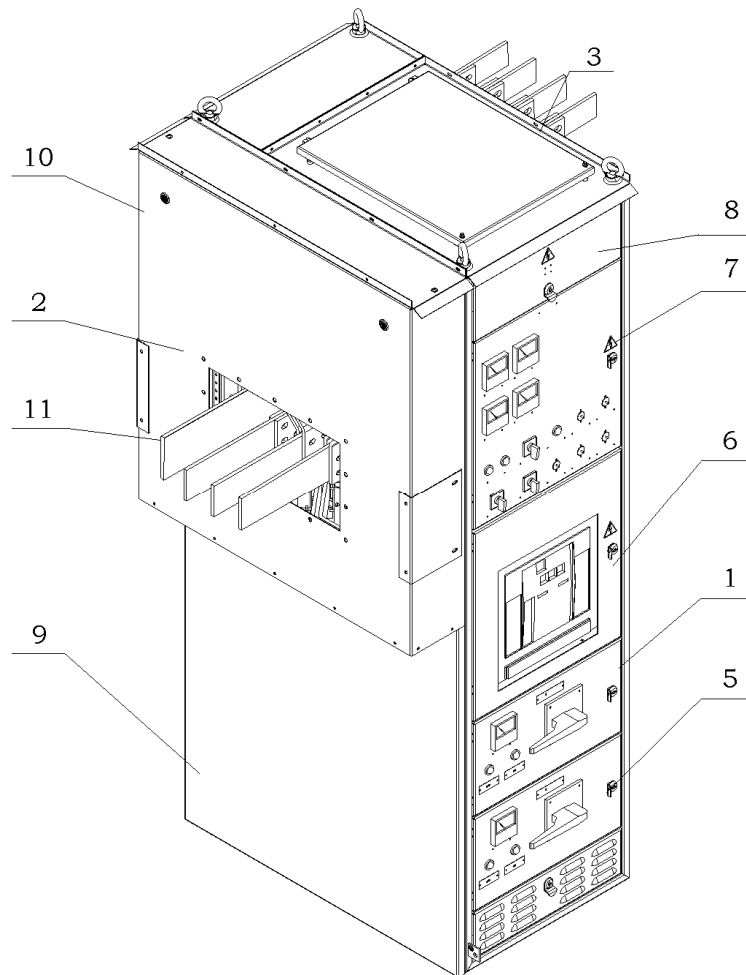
Конструктивное исполнение шкафа с выключателем рабочего ввода с установленным шинным узлом: 1 – шкаф с выключателем рабочего ввода; 2 – шинный узел для стыковки с силовым трансформатором; 3– отсек для сборных шин; 4 – клапан для разгрузки; 5 – отсек для силовых ячеек; 6 – отсек для вводного выключателя; 7 – отсек для релейного блока; 8 – отсек для шинок цепей питания к УВН и трансформатору; 11 – отсек для шин
